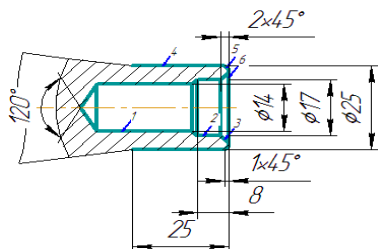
Задані поверхні тримача для обробки збірним інструментом
